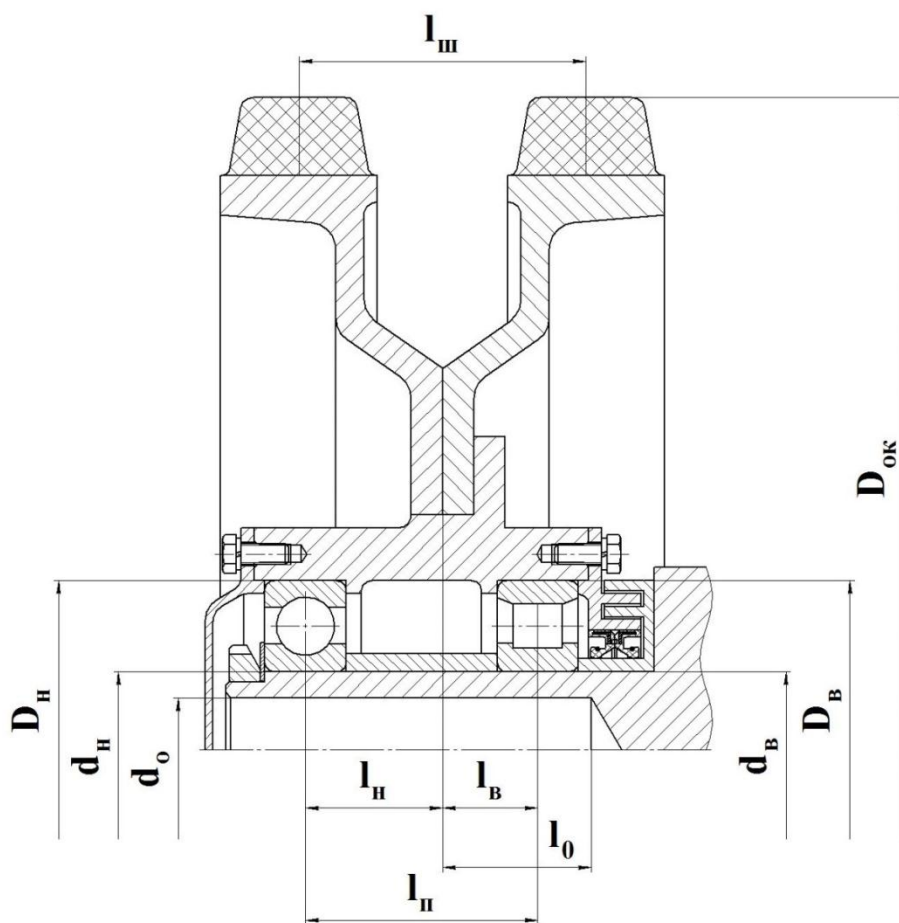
Расчетная схема подшипникового узла опорного катка
